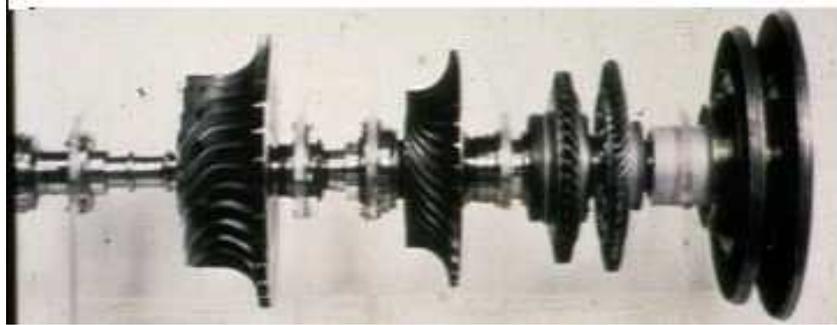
L'ensemble compresseur –turbine (rotor)
